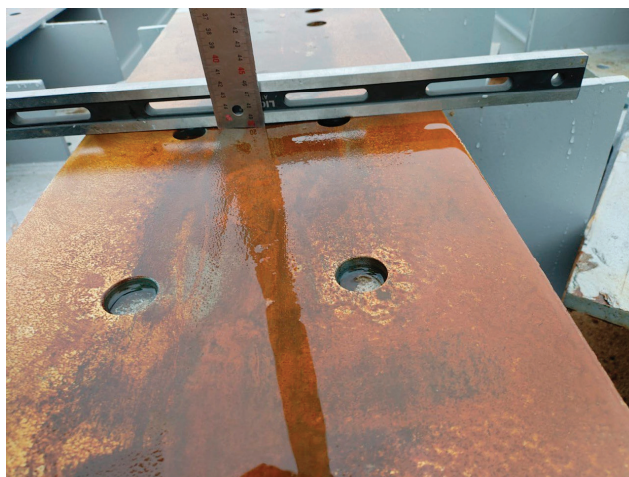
Замер грибовидности фрезерованной поверхности фланца с помощью поверочной линейки
